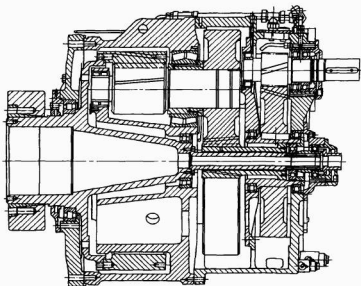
行星轴固定的三级圆柱齿轮传动齿轮箱
